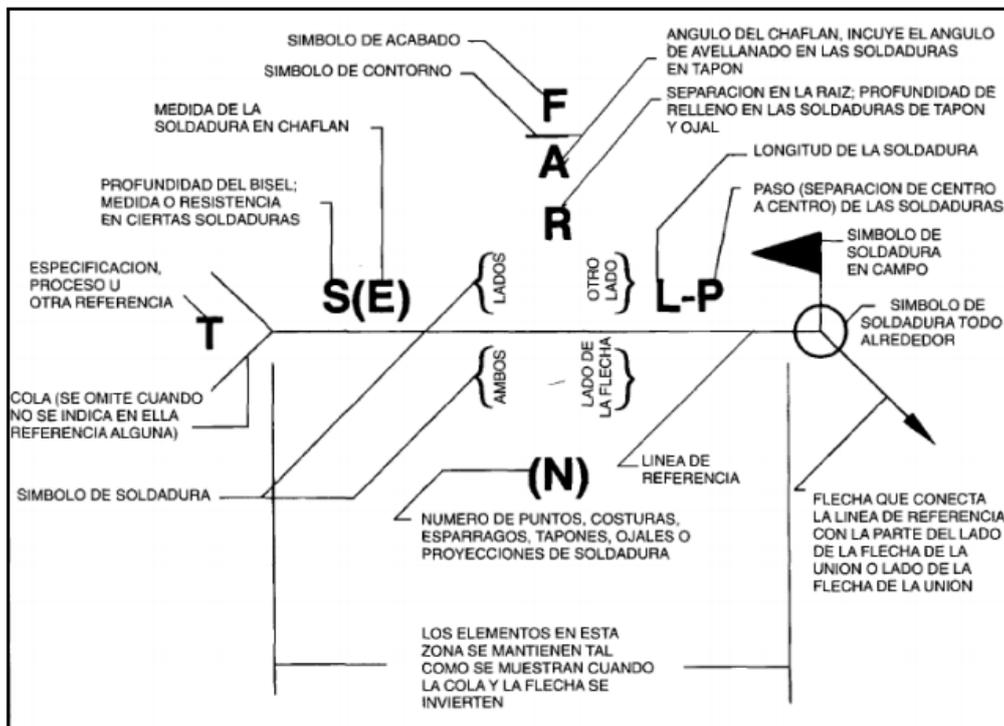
Estructura completa de la simbología de la soldadura.
